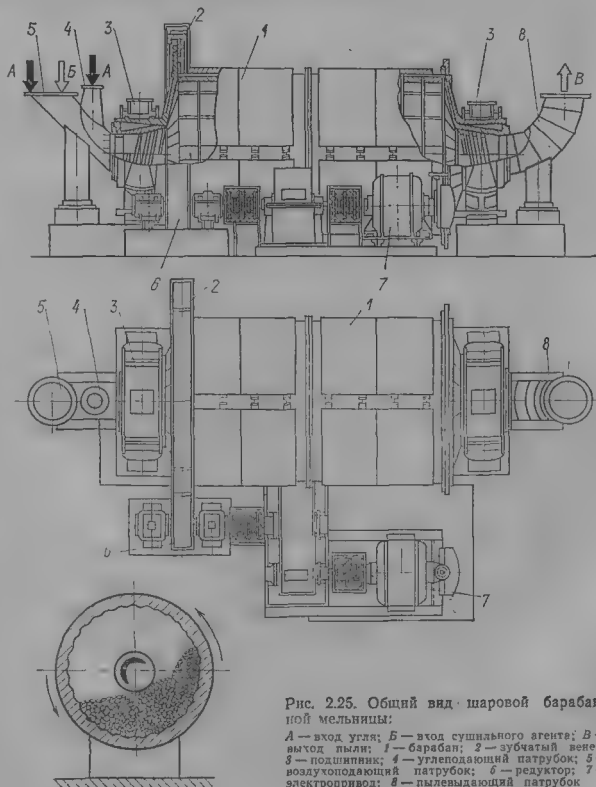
Общий вид шаровой барабанной мельницы:
